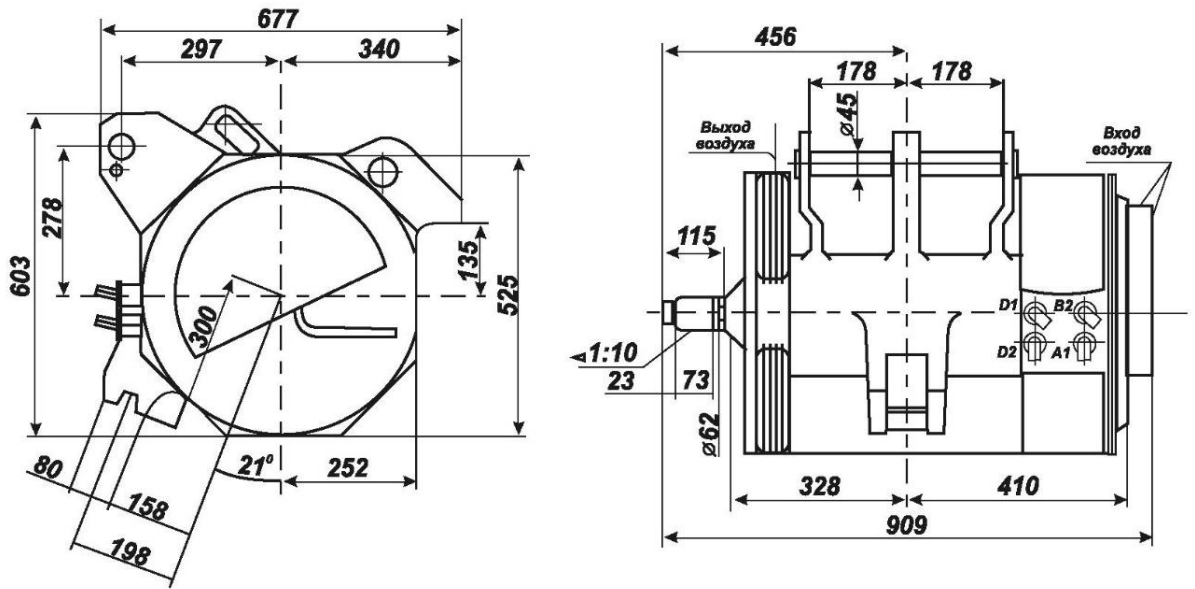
Габаритні та установочні розміри двигуна типу ДК117ДМ/ВМ
